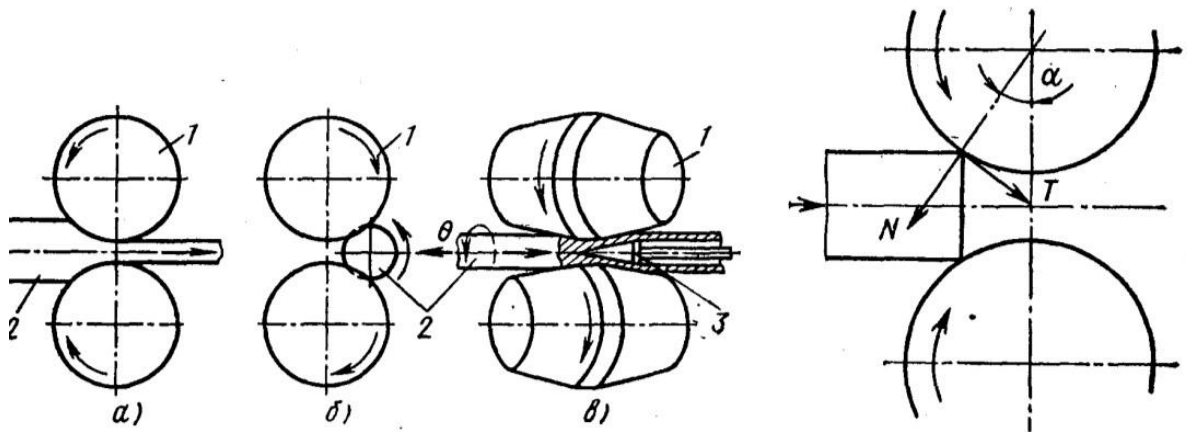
Види прокатки та схема дії сил у момент захоплення заготовки валками
